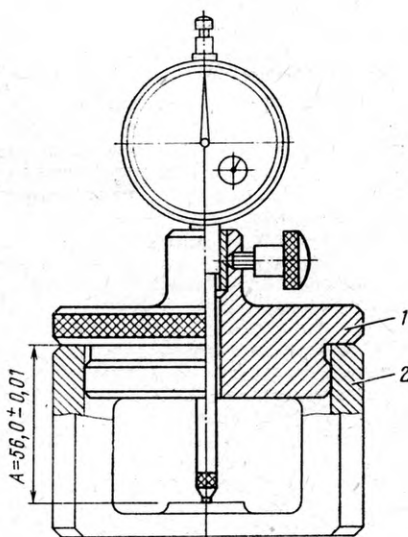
Индикаторное приспособление для настройки прибора ПР.722:
